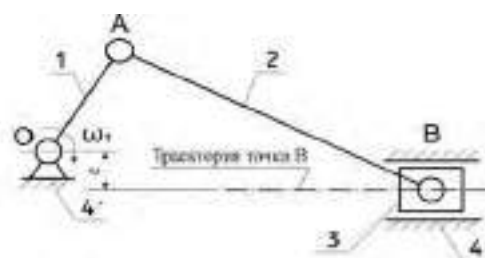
Кинематическая схема кривошипно-ползунного механизма
